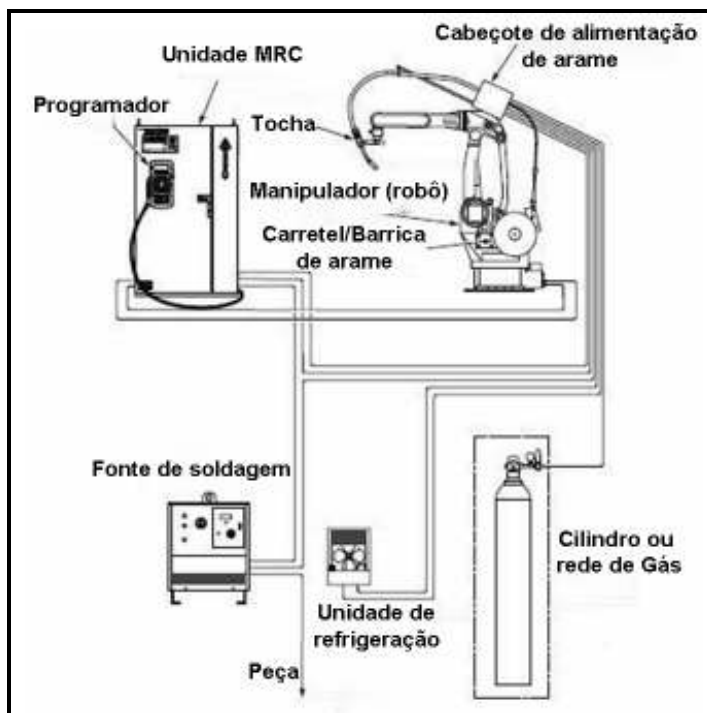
Desenho esquemático dos principais equipamentos utilizados no processo de soldagem robotizada MIG/MAG. (Motoman, 1995).
